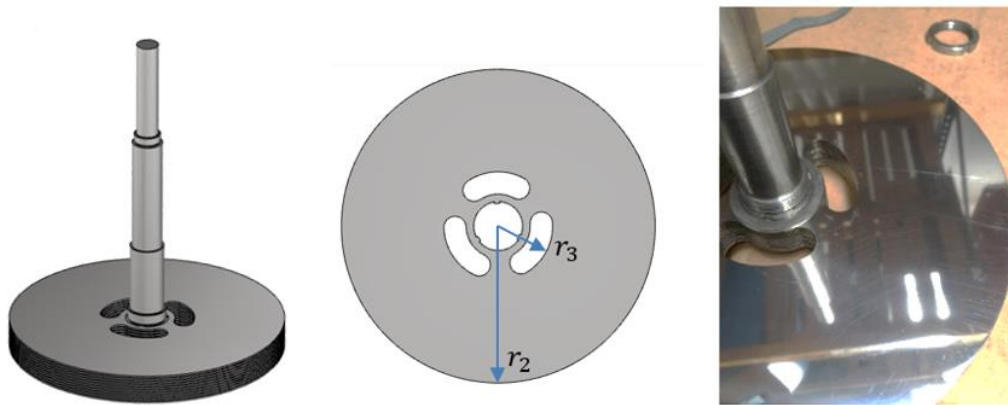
Dischi di rotore e loro calettamento sull'albero, vista reale e 3D
